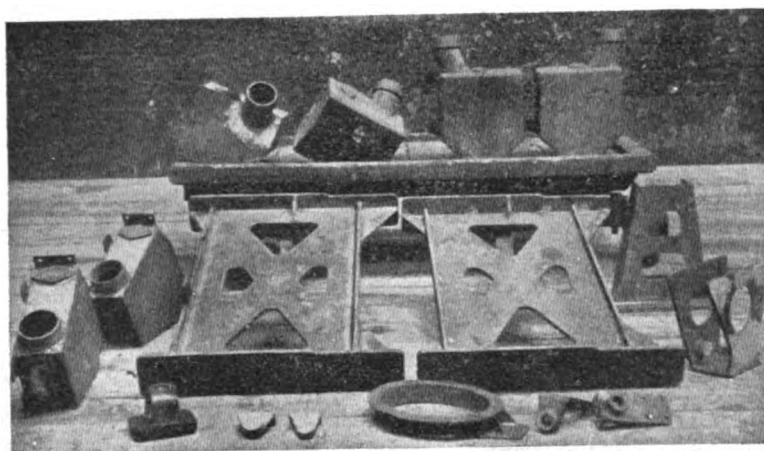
Saldatura elettrica di parti della locomotiva.
